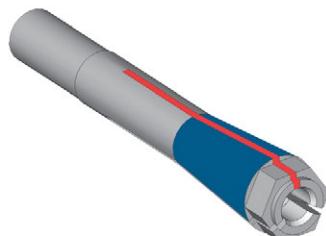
ENGRASAR LA PINZA DE SUJECIÓN; LA SUPERFICIE A LA QUE SE DEBE APLICAR GRASA APARECE MARCADA EN AZUL; LA RANURA QUE NO DEBE ENGRASARSE APARECE MARCADA EN ROJO
